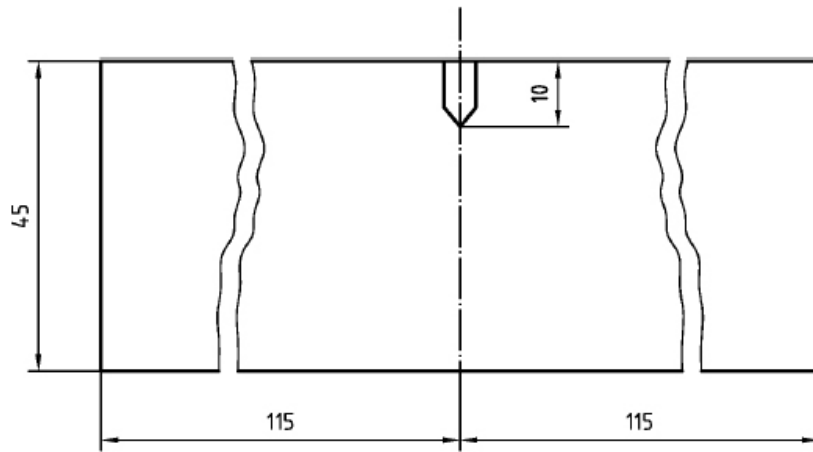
Posición y dimensiones de probetas para estudio del comportamiento a fractura del carril.
